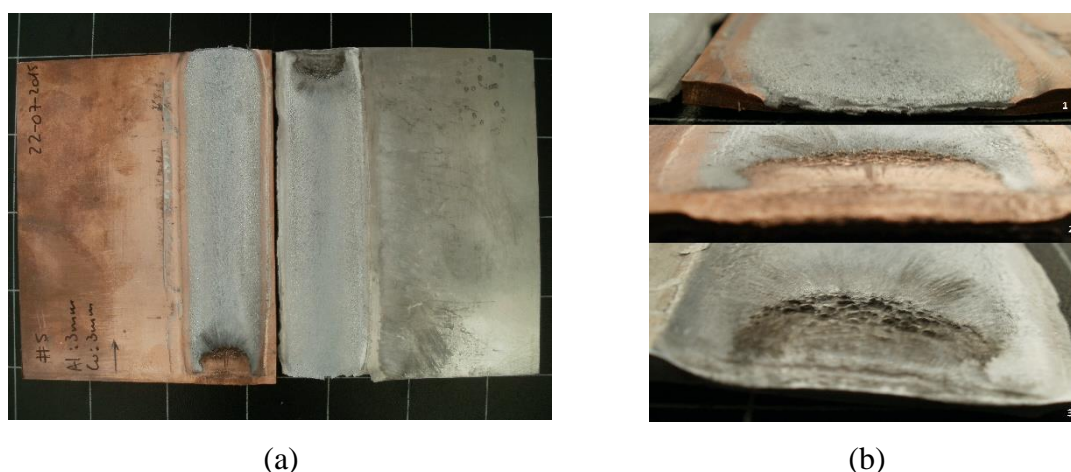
(a) Soldadura UEW3; (b) Detalhes da zona soldada.
